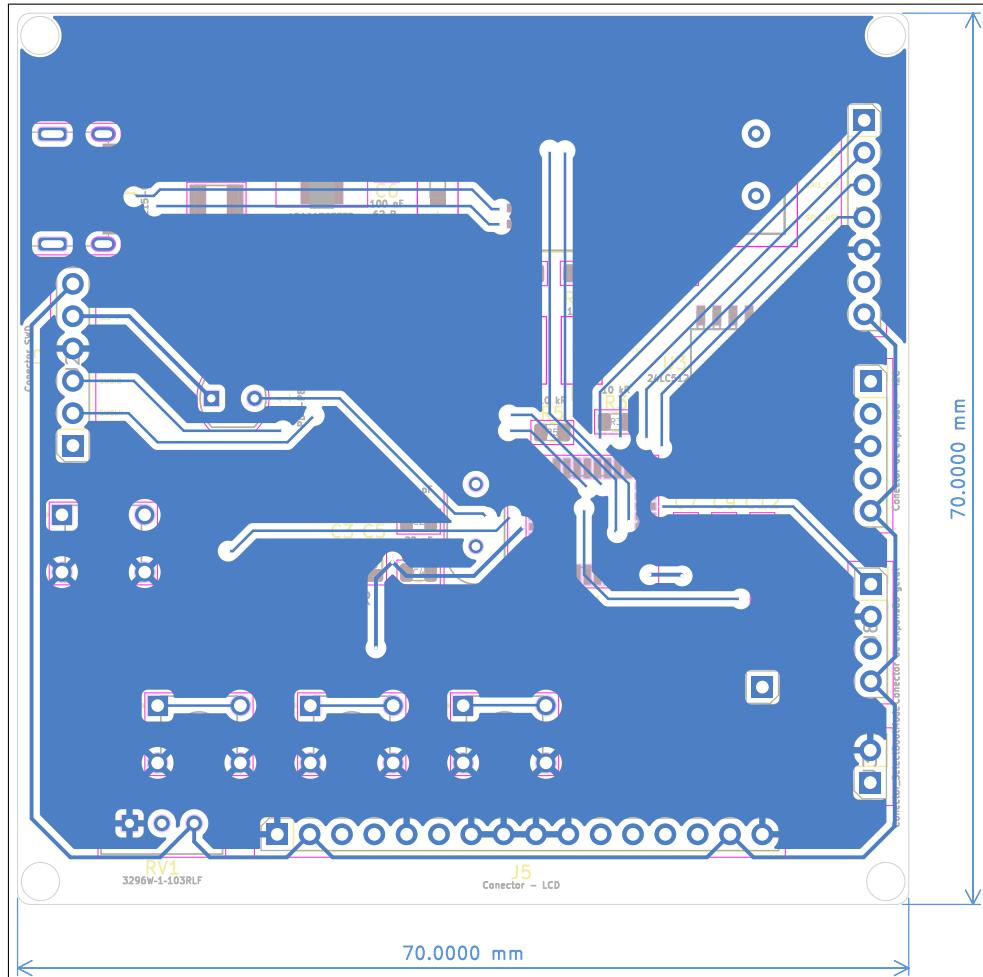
Camada inferior da placa de circuito impresso - Kicad
